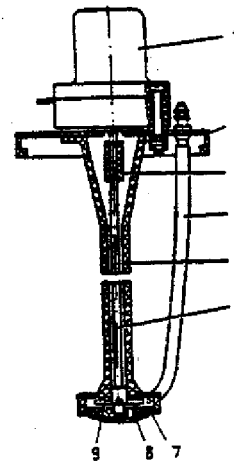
Bomba do lavador do pára-brisa: 1 - motor elétrico; 2 - tampa do reservatório; 3 - acoplamento; 4 - tubo de alimentação de líquido; 5 - corpo da bomba; 6 - árvore do rotor; 7 - apoio da árvore do rotor; 8 - anel com filtro de tela; 9 - rotor.
